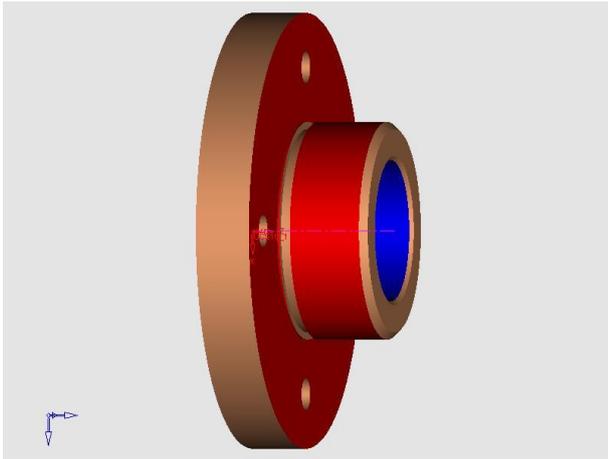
Модель заготовки, обрабатываемой на шлифовальной операции
